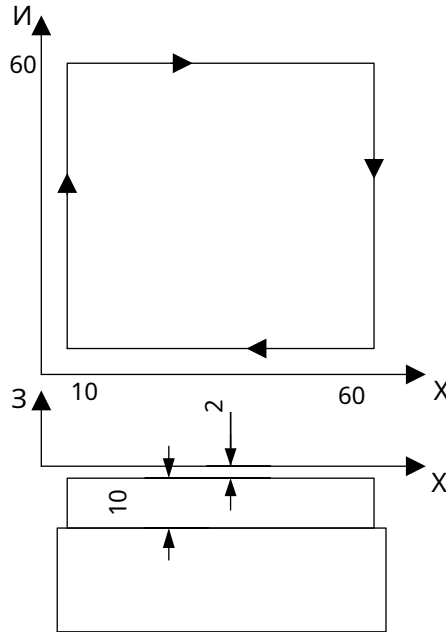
Эскиз 5 процесса обработки заготовки
